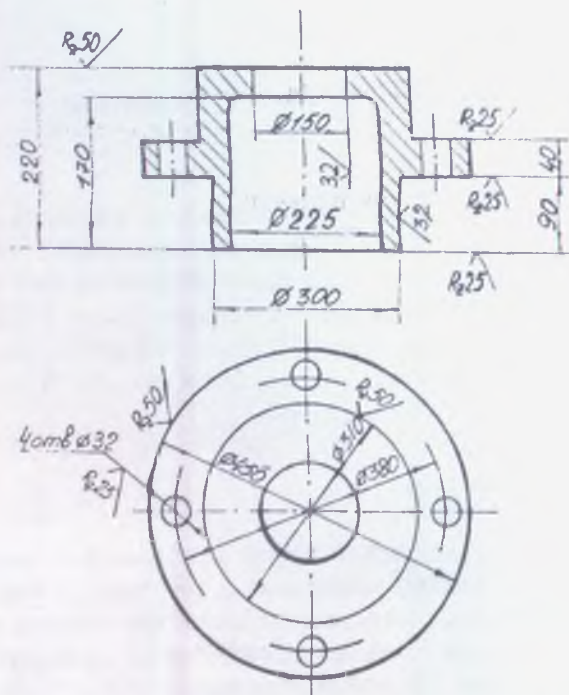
Чертеж детали "крышка" (Сталь 45Л)
